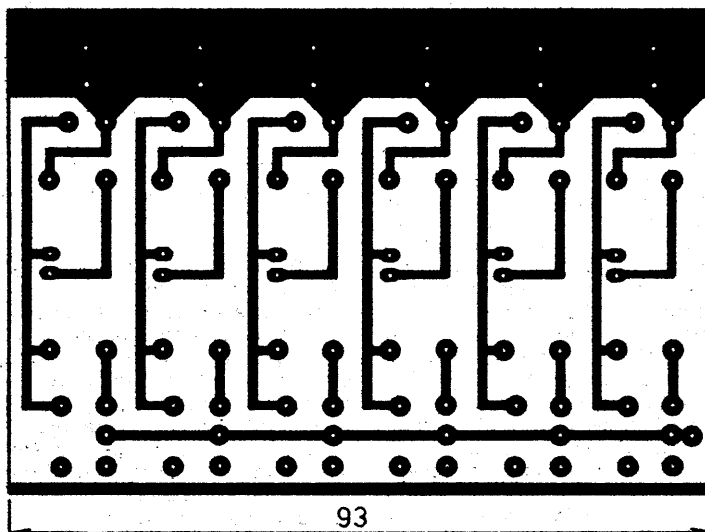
Deska plošných spojů V325 vř milivoltmetru
